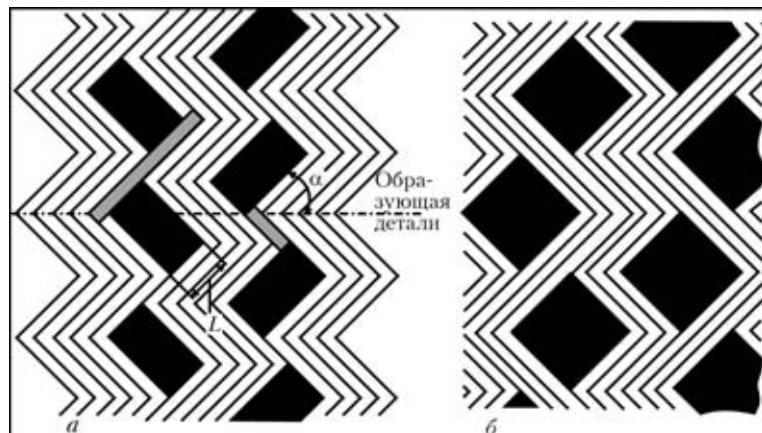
Схемы (а, б) формирования лунок при наплавке рабочей поверхности швами зигзагообразной формы
